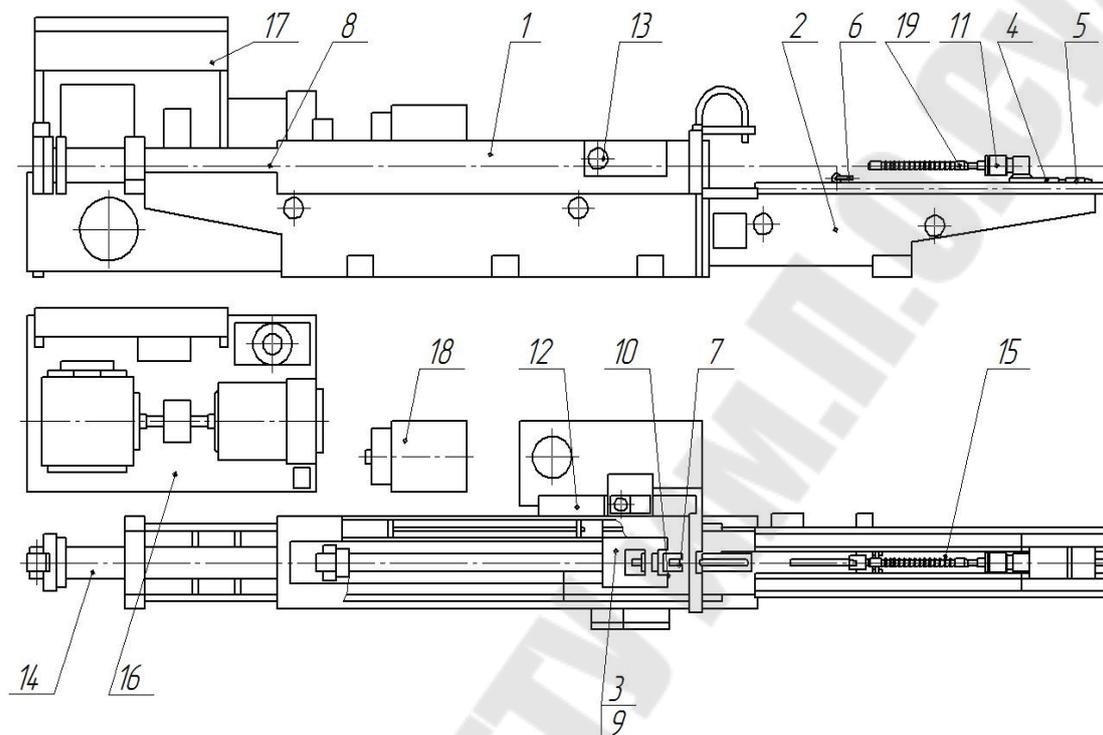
Схема горизонтального протяжного станка модели 7Б56:
